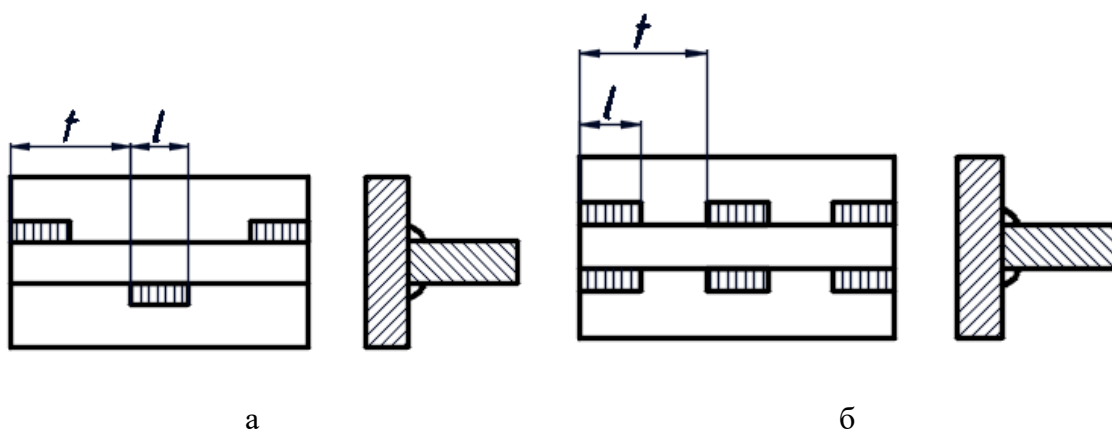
Образец выполнения сварных швов по протяженности.
